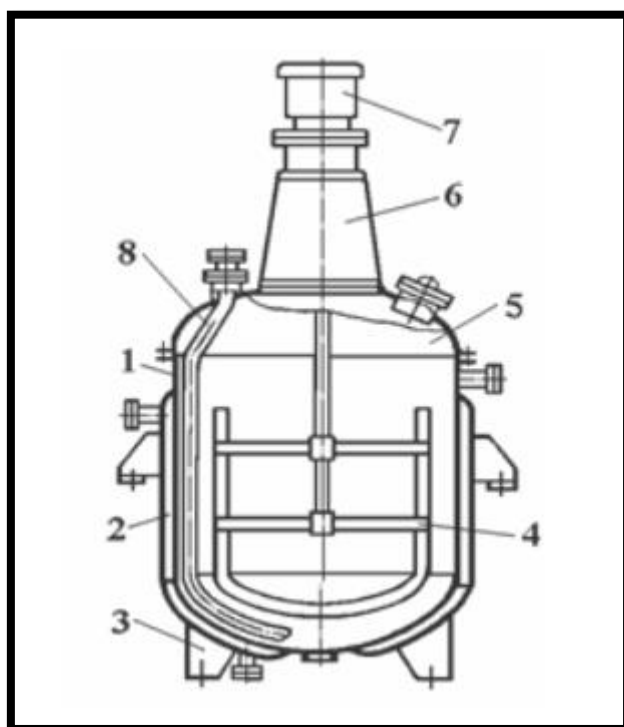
Будова реакційного апарату з сорочкою та рамною мішалкою: 1 - корпус; 2 - сорочка; 3 - опора; 4 - мішалка рамна; 5 - кришка знімна; 6 - редуктор; 7 - електродвигун; 8 - труба для передавлювання середовища
